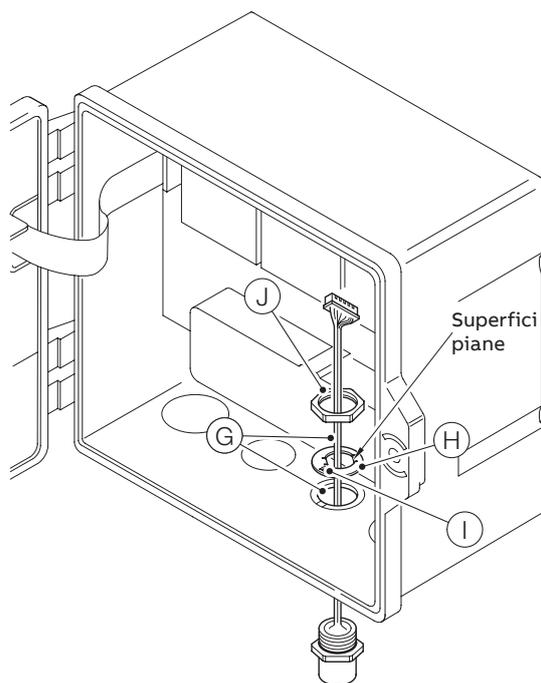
Preparazione degli elementi di fissaggio dei cavi dei connettori passanti EZLink
